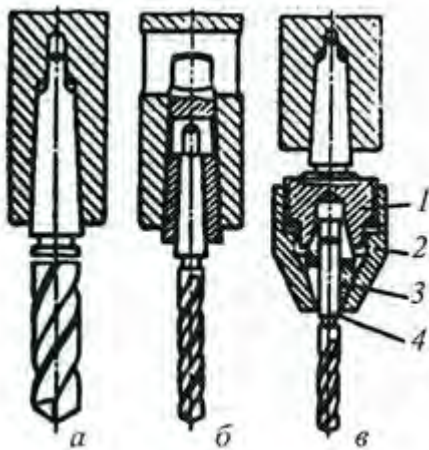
Схеми закріплення інструментів у шпинделі свердильного верстату
